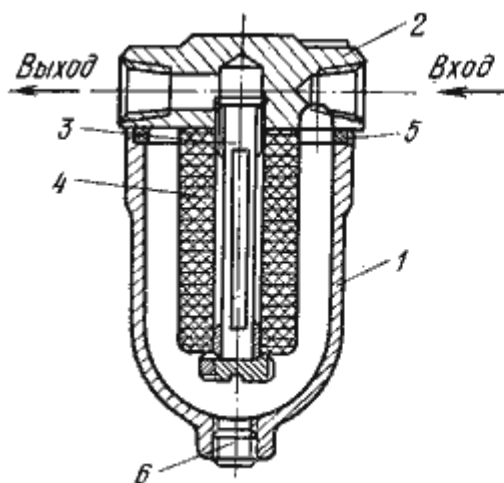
Войлочный фильтр типа Г43: 1 - корпус; 2 - крышка; 3 - перфорированная труба; 4 - фильтрующие элементы
